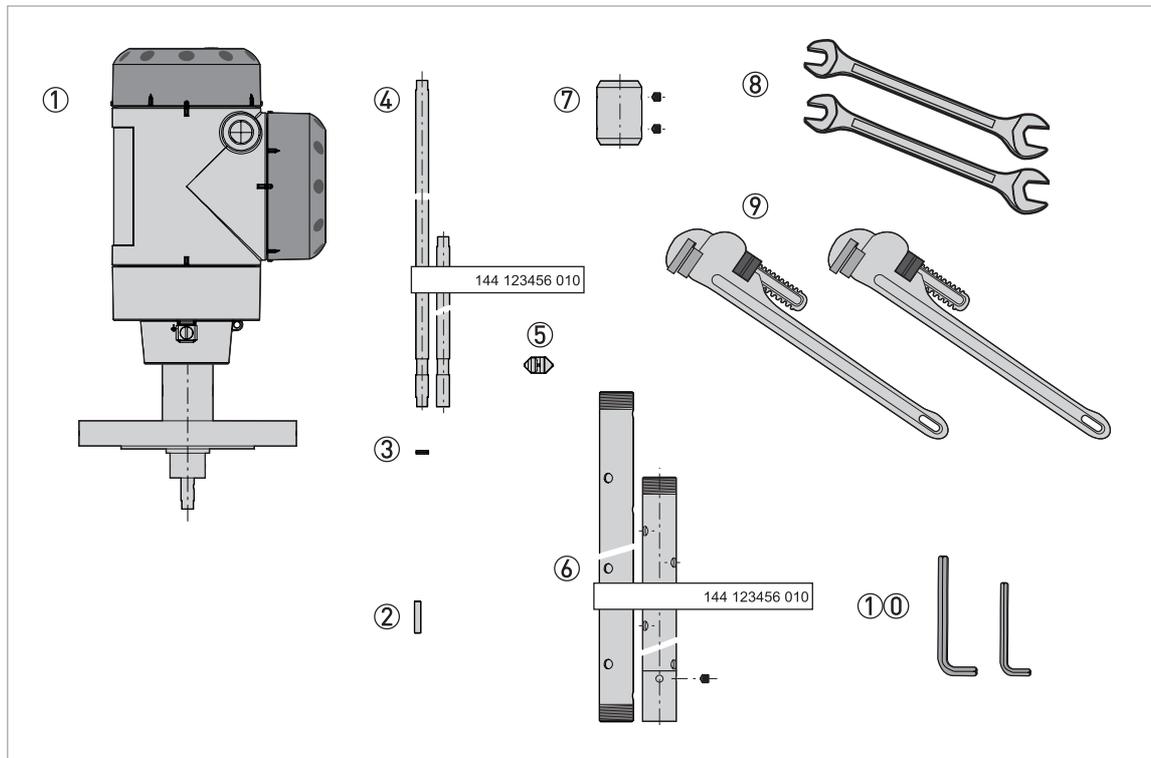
Equipement requis pour monter la sonde coaxiale
